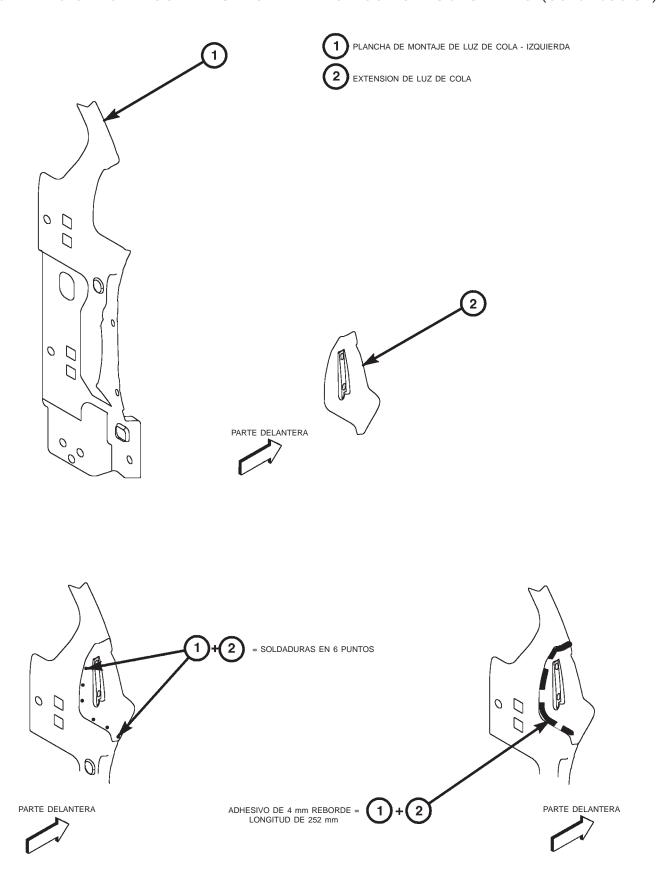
PLANCHA DE MONTAJE DE LAS LUCES DE COLA
